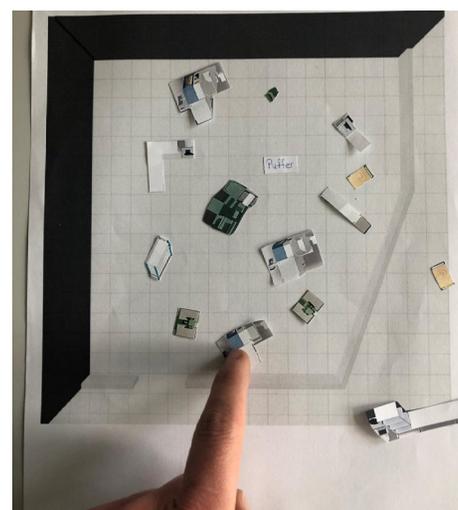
Cardboard Engineering zur Layoutoptimierung
